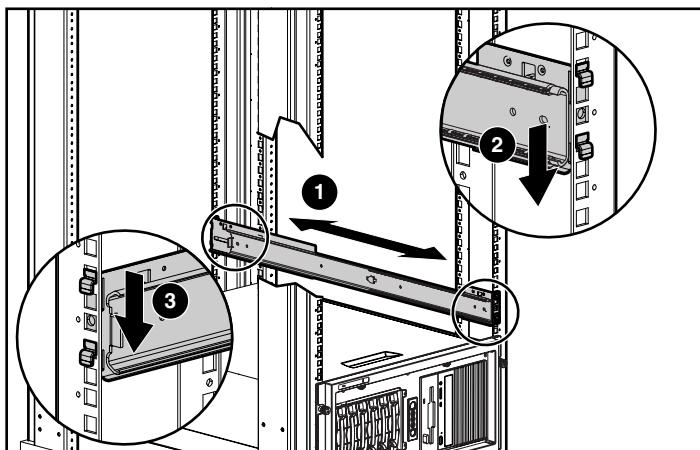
Fixação do conjunto deslizante do suporte de montagem no rack
